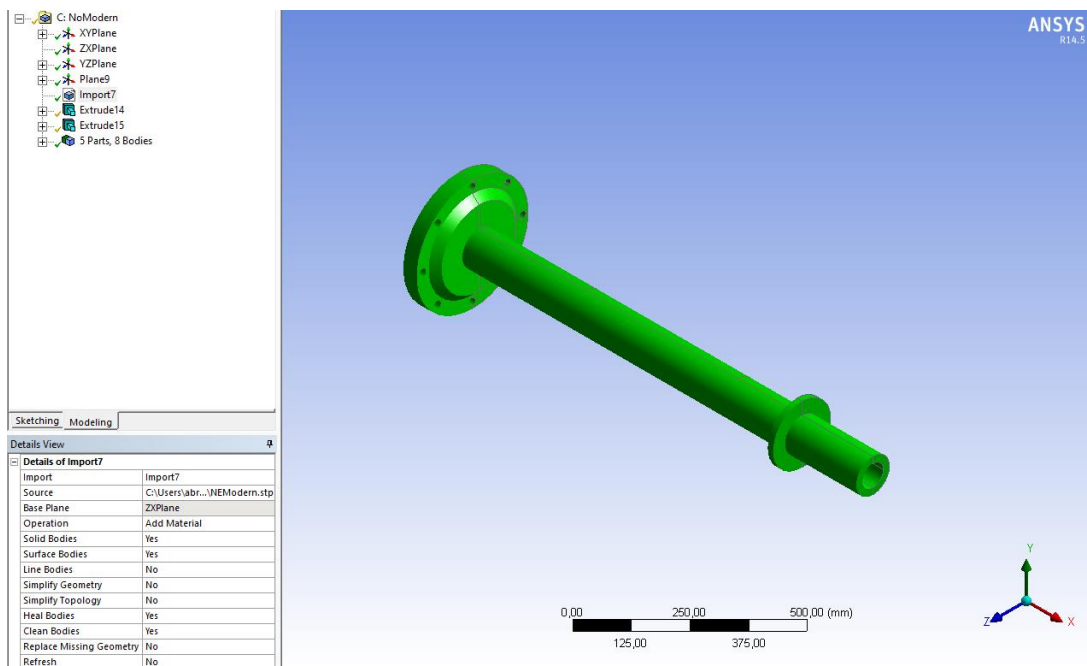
Початкова геометрія корпусу екструдера.
